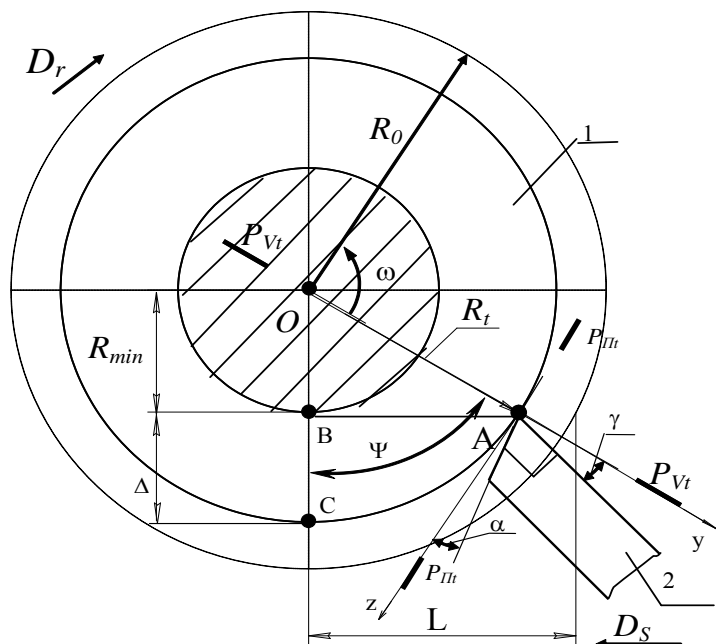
Кинематическая схема процесса тангенциального точения с прямолинейной подачей: 1 – заготовка; 2- инструмент
